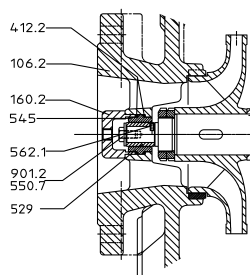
Desmontagem do rolamento deslizante - tubagem de aspiração axial
